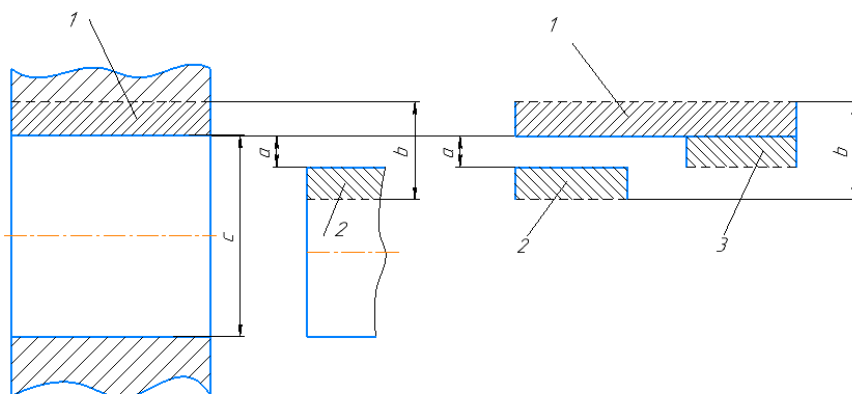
графическое представление посадки с зазором: 1- интервал допуска отверстия; 2– интервал допуска вала; случай 1 - верхний предельный размер вала ниже, чем нижний предельным размером отверстия, наименьший зазор больше нуля; 3 - интервал допуска вала, случай 2: верхний предельный размер вала совпадает с нижним предельным размером отверстия, наименьший зазор равен нулю; a – наименьший зазор; b – наибольший зазор; c – номинальный размер, равный нижнему предельному размеру отверстия
